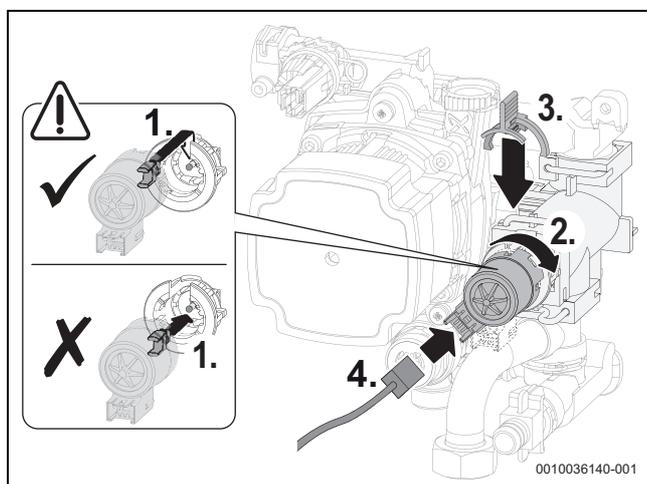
Installation du moteur dans la vanne sélective (variante sans vis)
